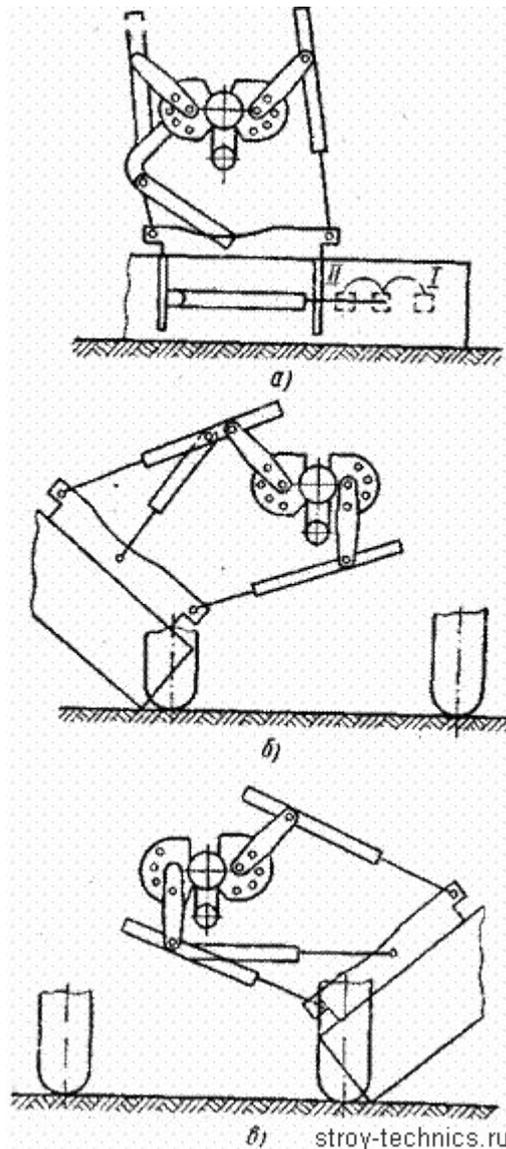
Схема положений рычагов подвески тяговой рамы с отвалом (вид из кабины):
